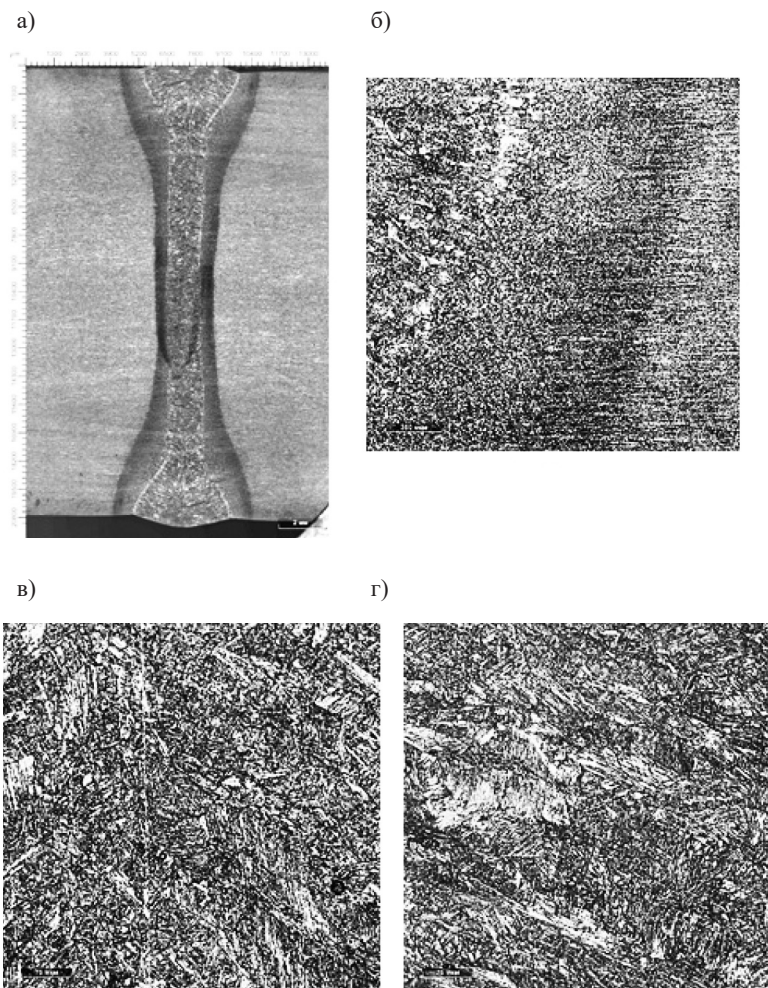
Лазерный шов образца стали марки 10XCHD:
